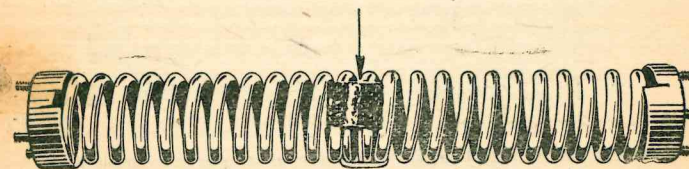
Поломка ограничительной пластинки пружины (стрелкой указано место сварки пластинки)
